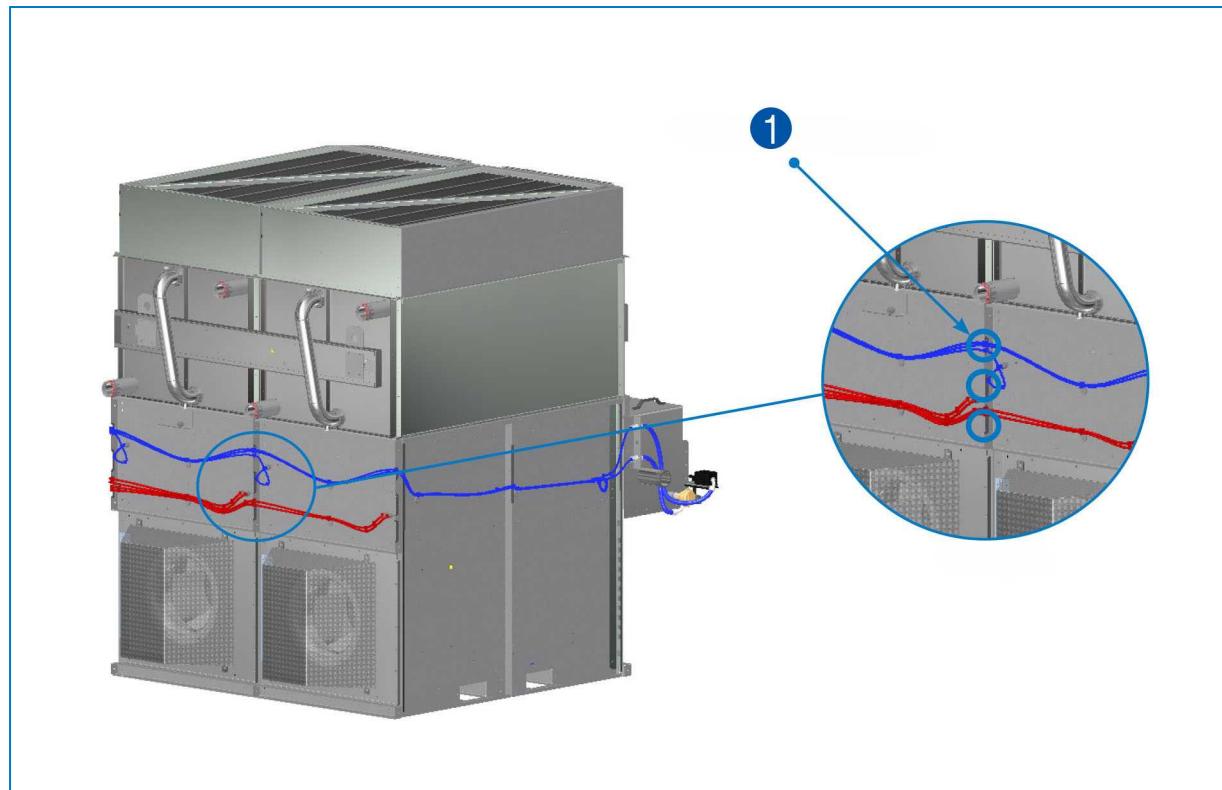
Провод электропитания вентилятора (красного цвета) — 1. Прорези для прокладки проводов
